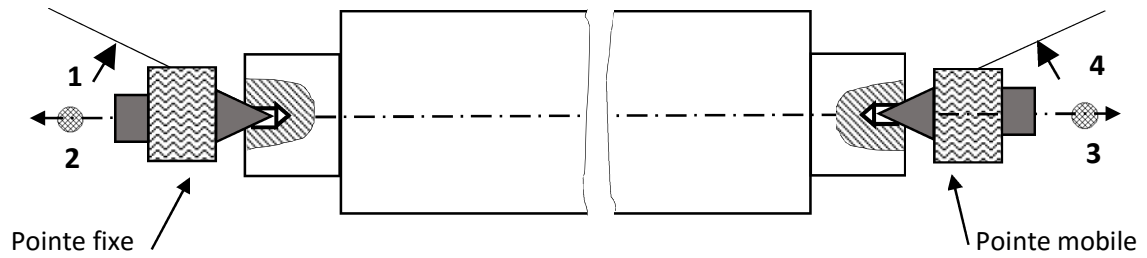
Mise en position d'un cylindre long en montage entre pointe sur un tour et utilisation du doigt pousse toc.
